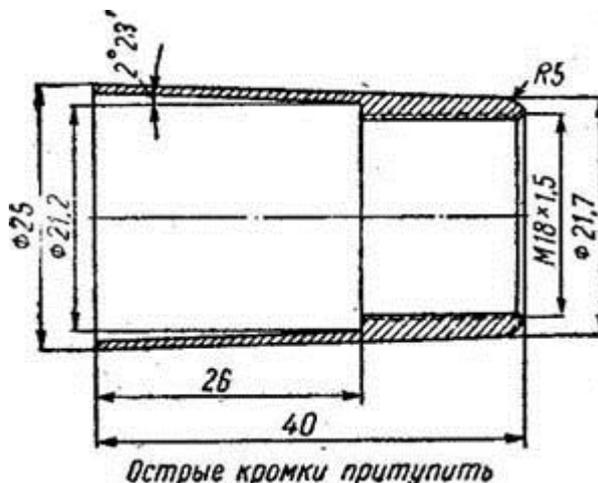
Приспособление для установки сальника левой цапфы коленчатого вала
